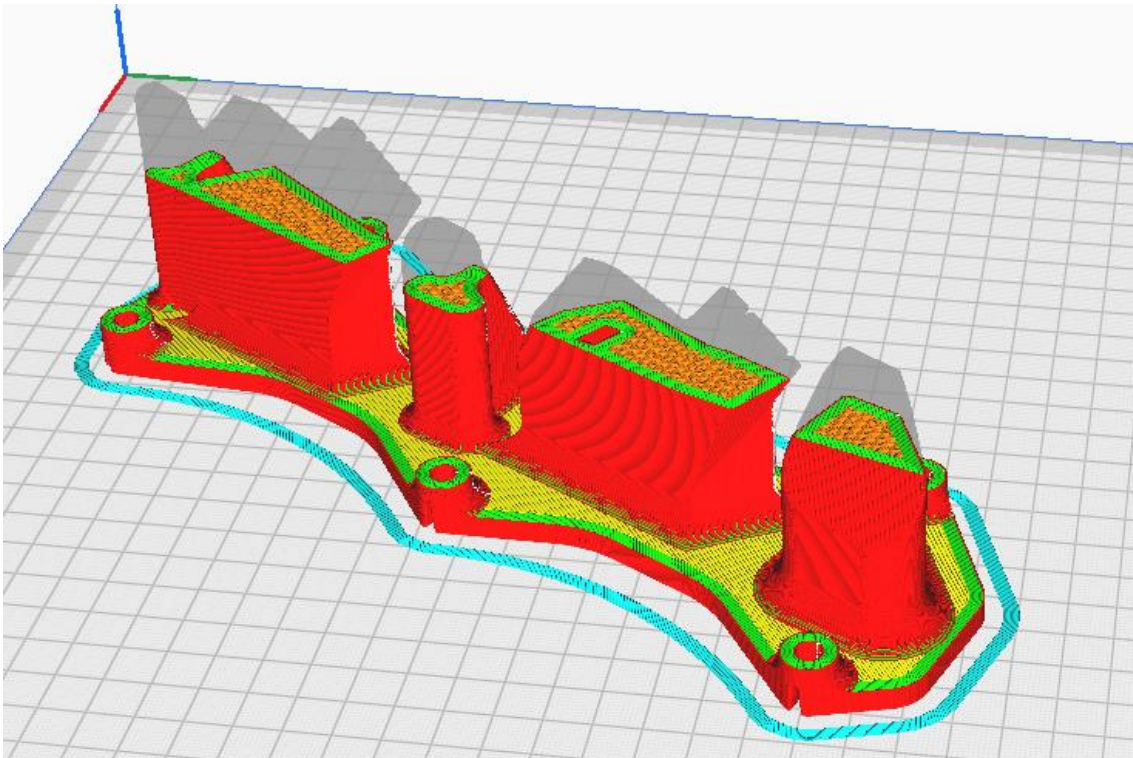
Vista módulo 1 del utillaje para pieza 4 en el laminador de Ultimaker Cura
